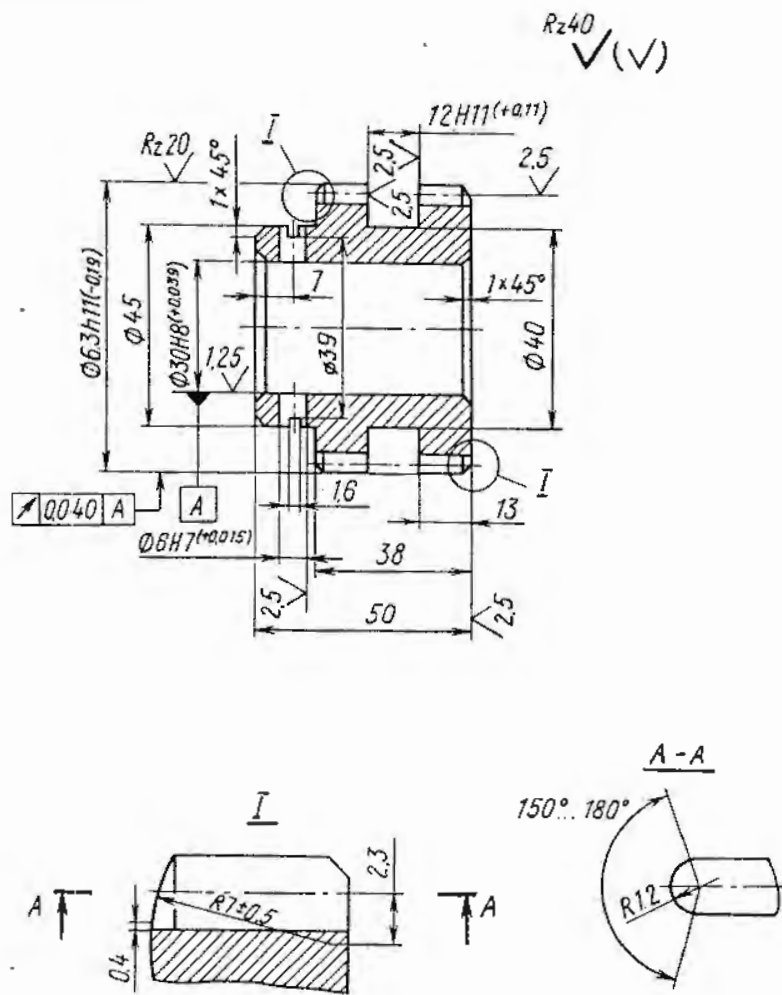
Колесо зубчатое, деталь № 3Л722А.322.402 НRC 28...30
